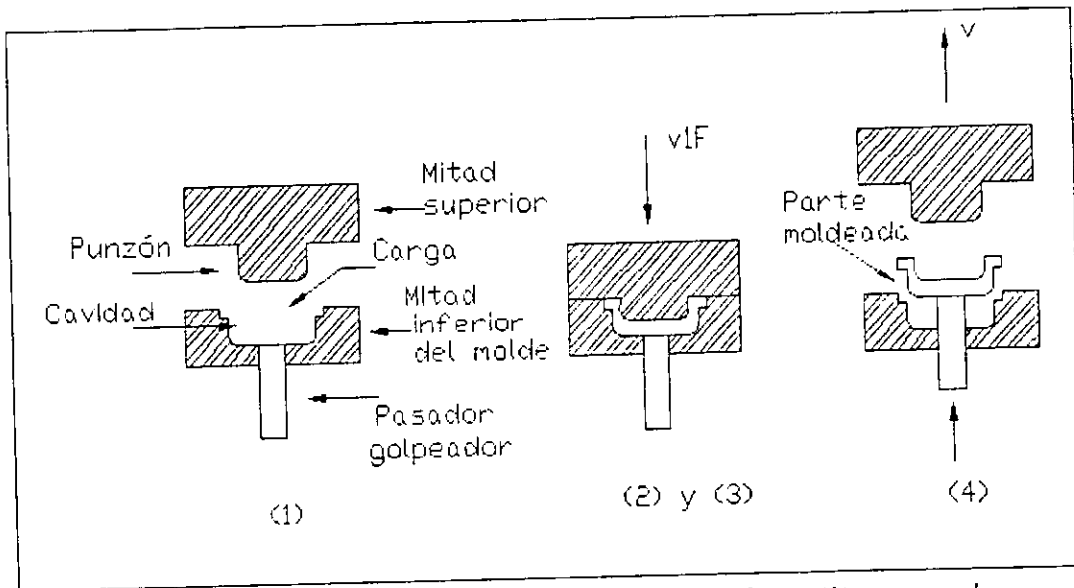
Moldeo por compresión para plásticos termofijos; (1) se pone la carga, (2) y (3) la carga se comprime y cura, y (4) la parte se expulsa y se retira.
